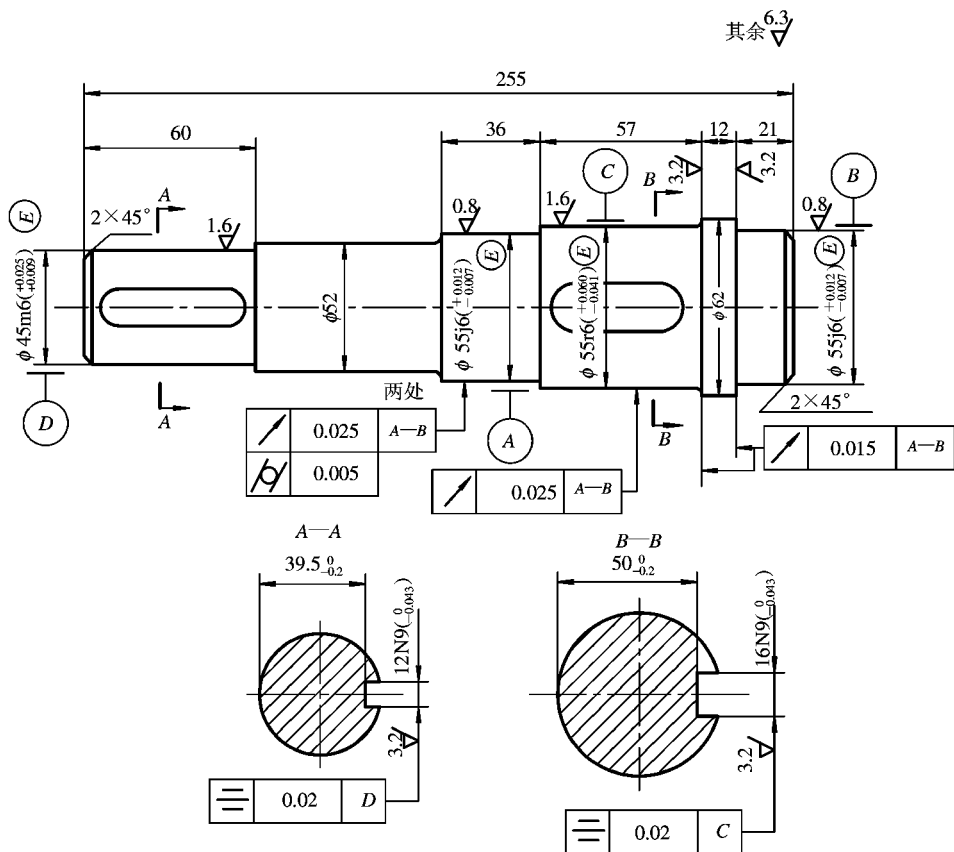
减速器输出轴的尺寸、形位、表面粗糙度的公差要求
